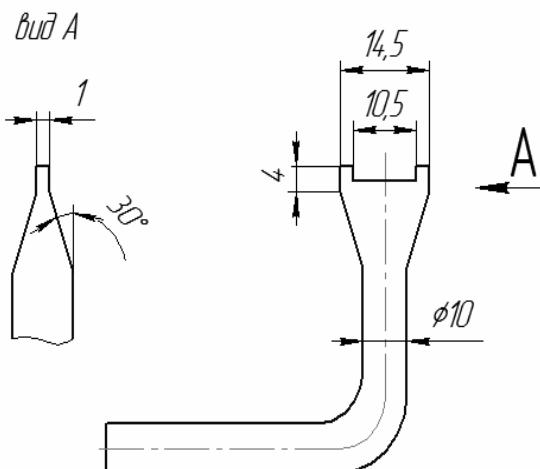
Специальная отвертка для разборки и сборки клапанов бустера.
